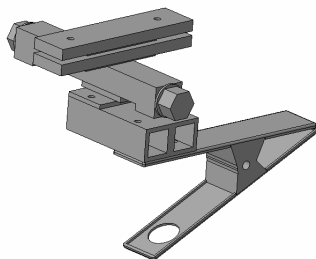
Внешний вид конструкции одного плеча разделённого токоподвода
